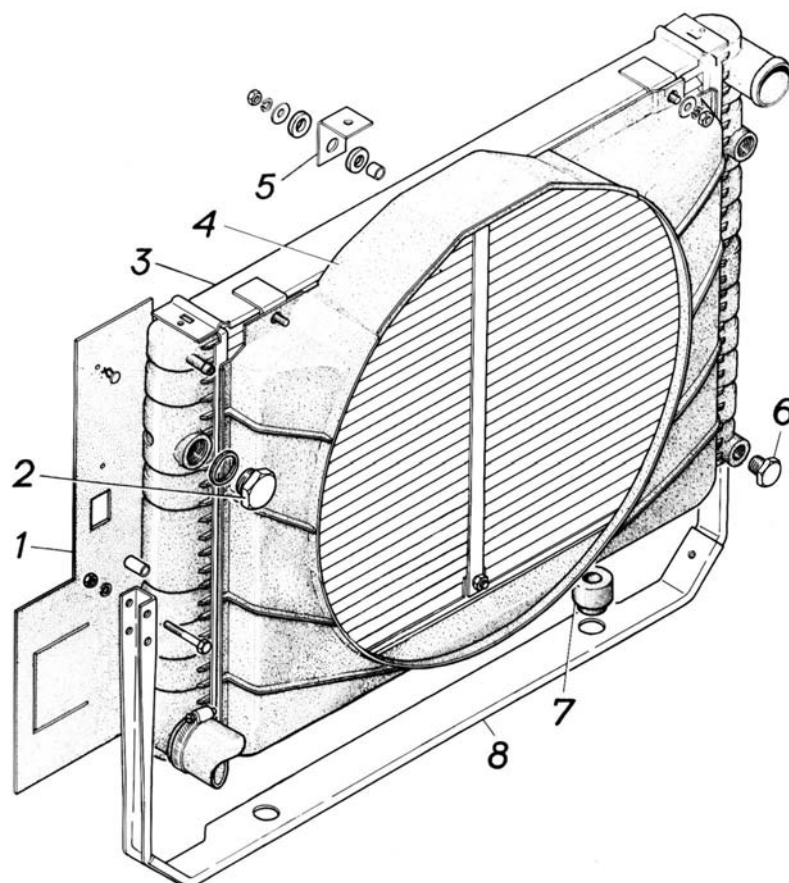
Радиатор: 1 - уплотнитель; 2 - пробка; 3 - радиатор; 4 - кожух вентилятора; 5 - кронштейн; 6 - сливная пробка; 7 - амортизатор; 8 - рамка
